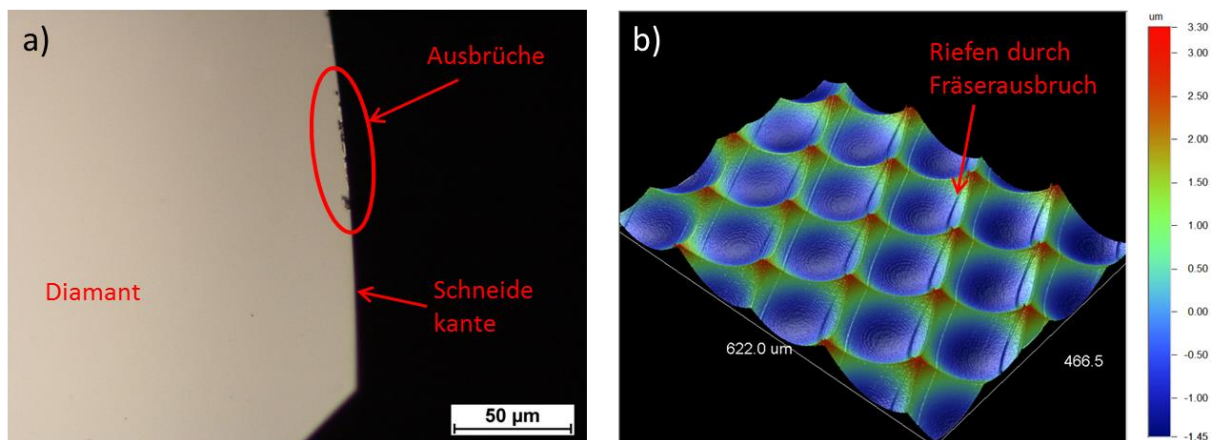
a) Schneidekante eines Diamantfräasers mit Ausbrüchen, b) resultierende Riefen auf der Oberfläche gefräster Mikrolinsen
